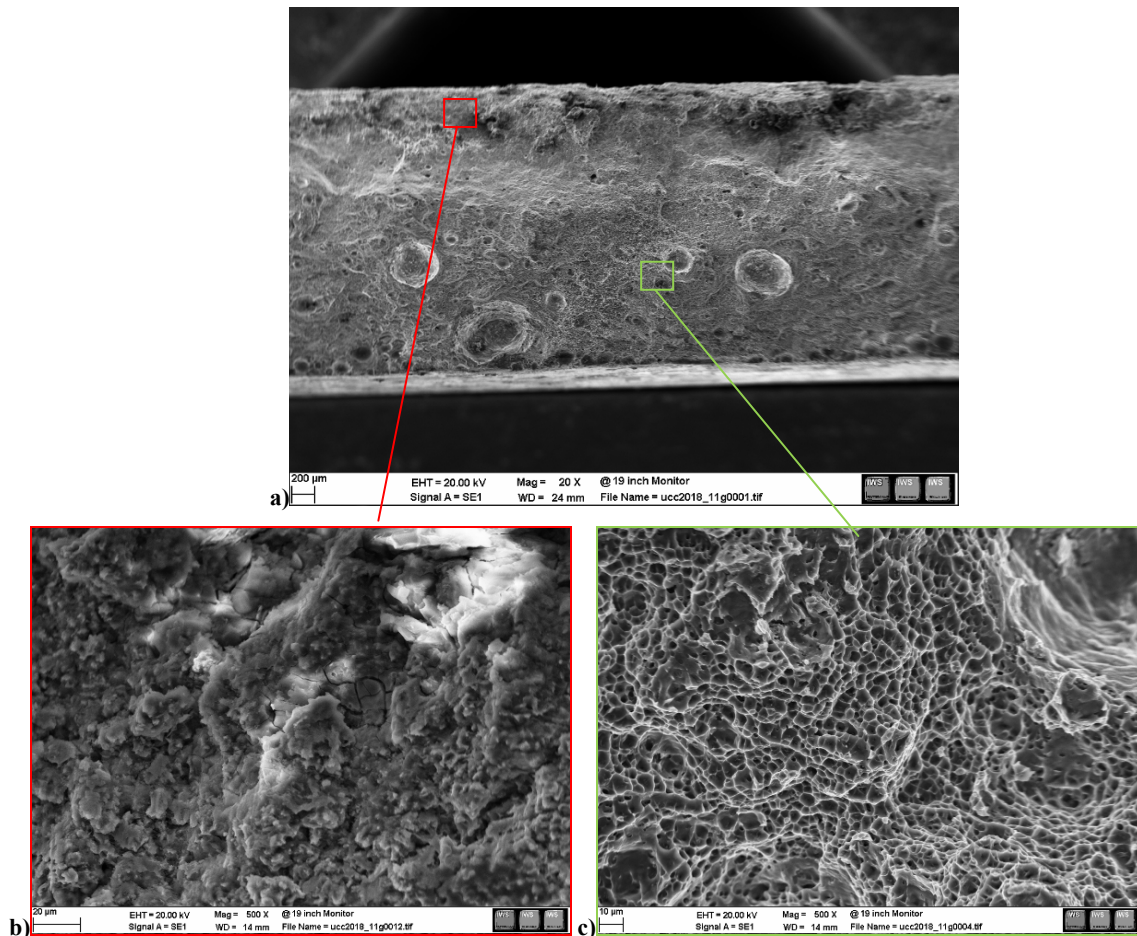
REM SE Aufnahmen einer AW-5083-O/AlMg5 Bruchfläche nach 480h NSS Test a) Aufnahme Bruchfläche im Schweißgut AlMg5 b) Detail vom Korrosionsbelag c) duktiler Bruchflächenbereich (Waben)
